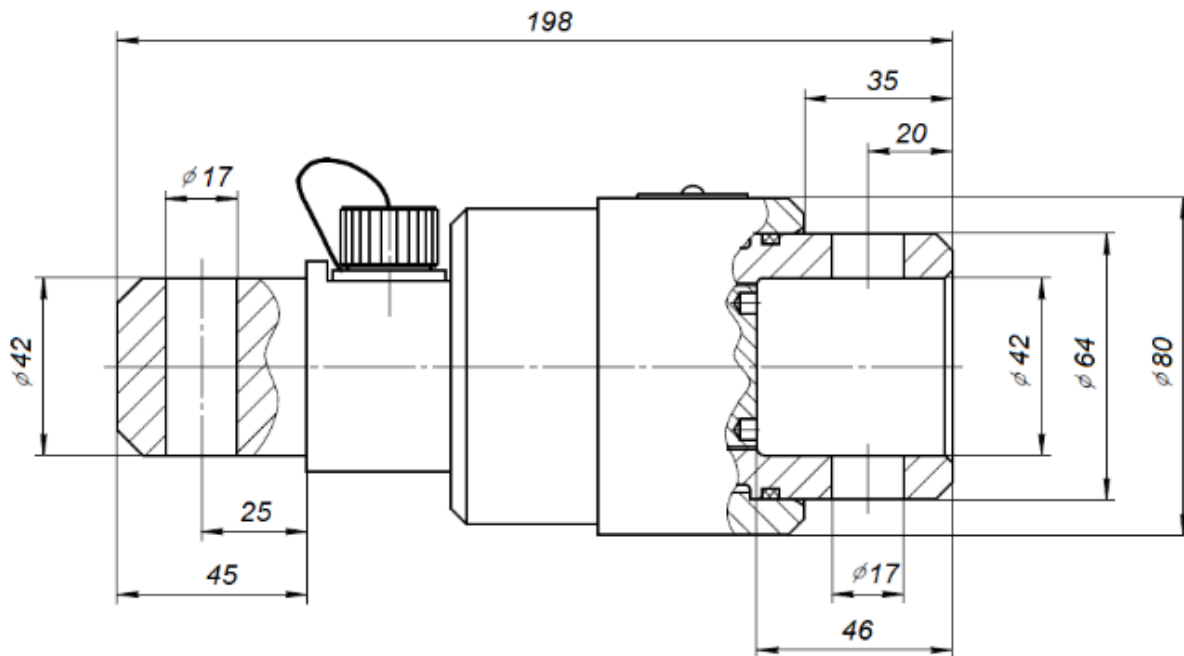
Габаритные и присоединительные размеры ДН-130В(Ш)
